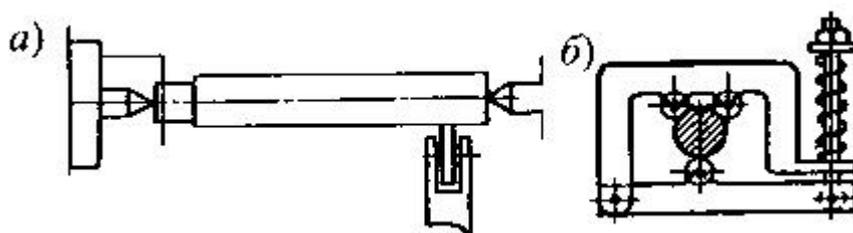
Приспособление для обкатывания цилиндрических поверхностей: а — с одним роликом; б — с тремя роликами
